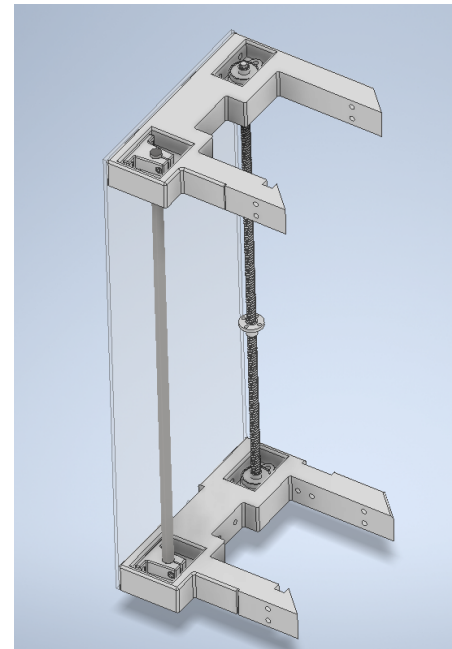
Cojinete empleado para sujetar el tornillo sin fin.
